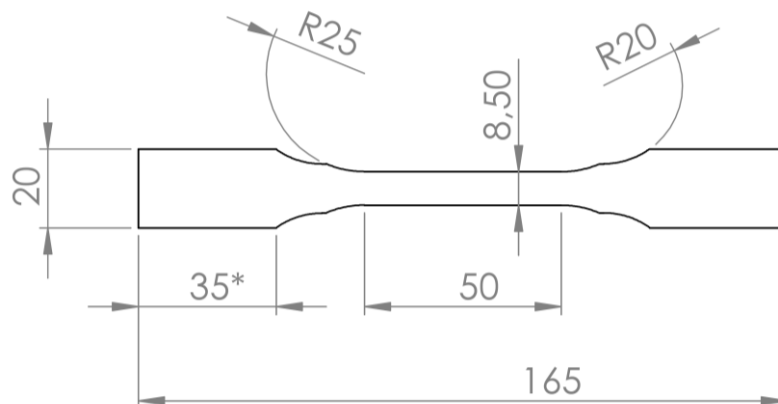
Geometrie der Zugversuch-Probe nach [59]
